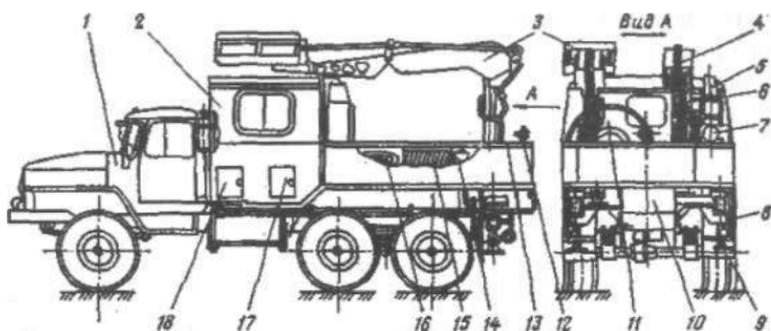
Агрегат 2АРОК для обслуживания станков-качалок:
